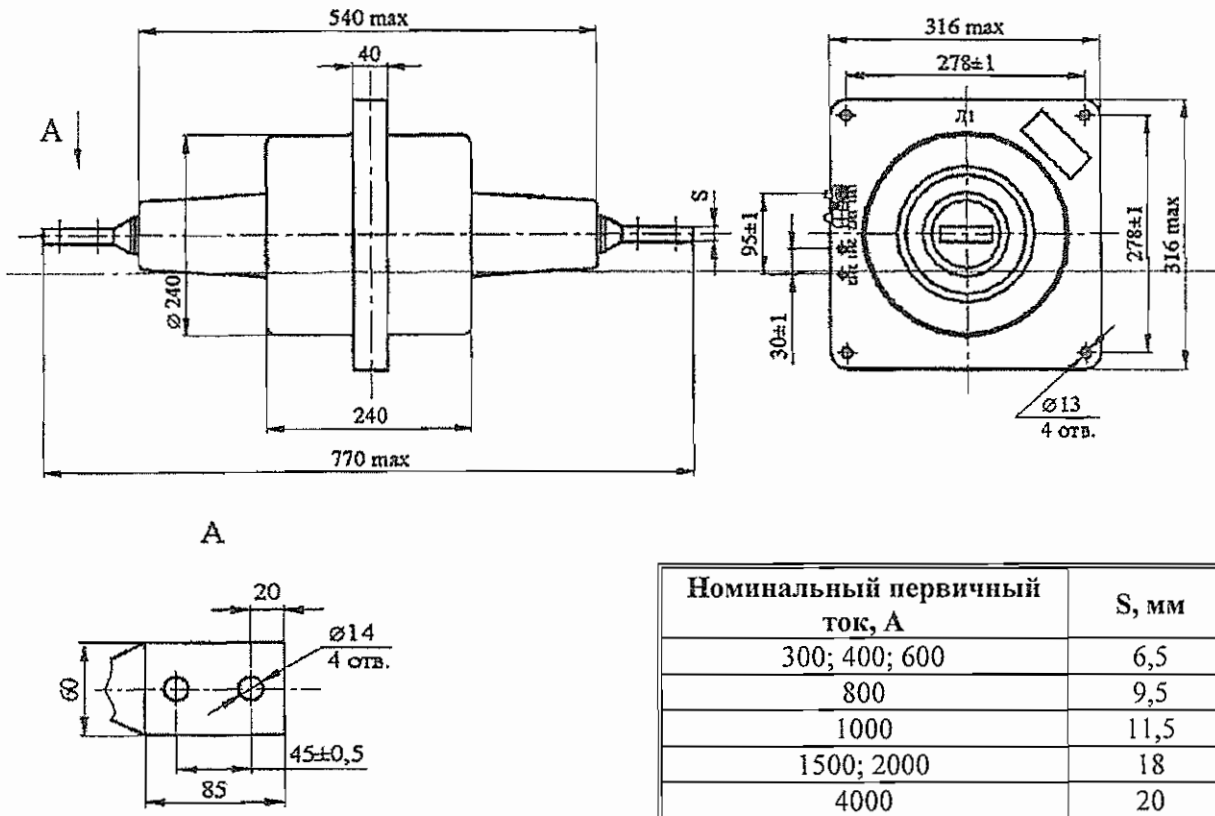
Общий вид, габаритные, установочные и соединительные размеры трансформаторов тока ТПЛ-20
